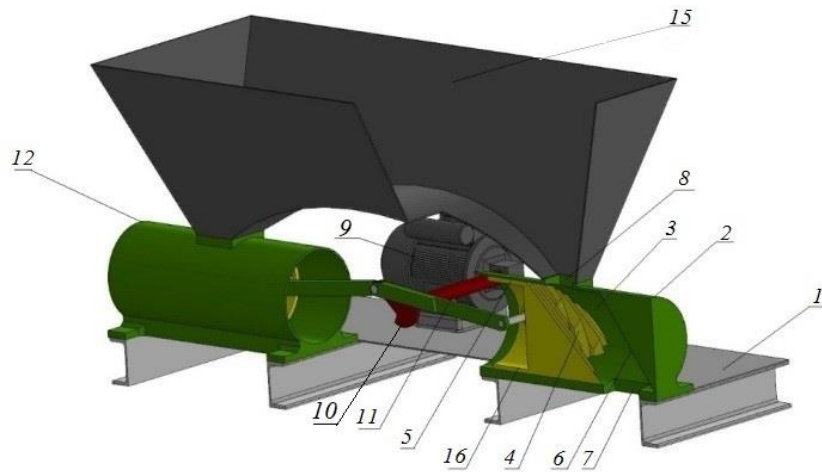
Общий вид измельчителя кормовой свёклы
